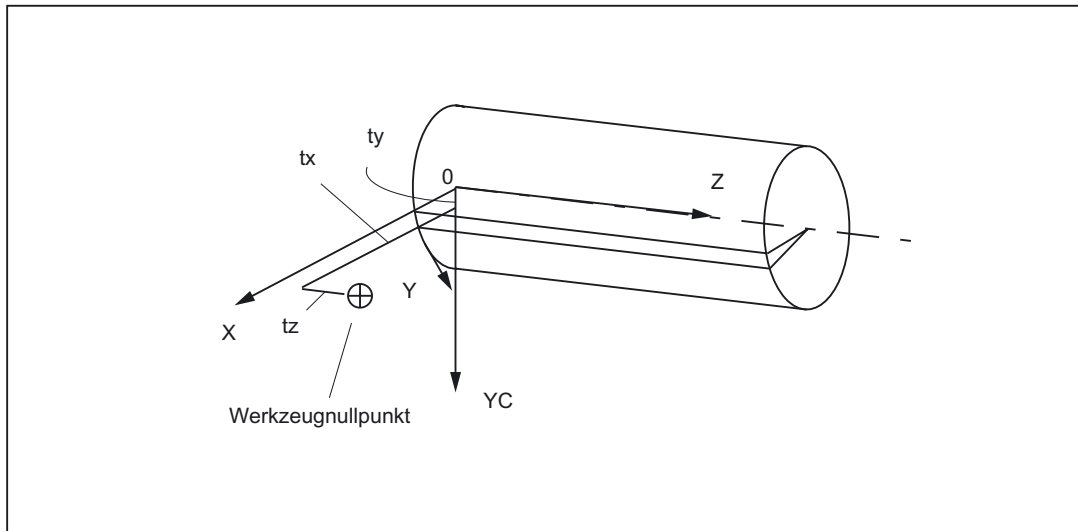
Lage des Werkzeugnullpunktes zum Nullpunkt der Maschine
